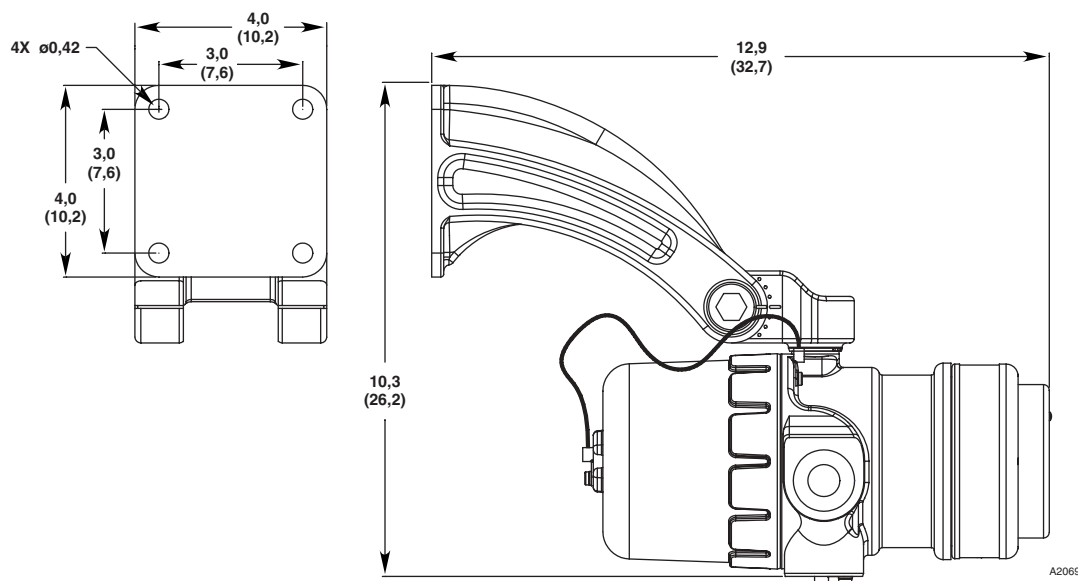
Abmessungen der Halterung Q9033B in Zoll (cm)
